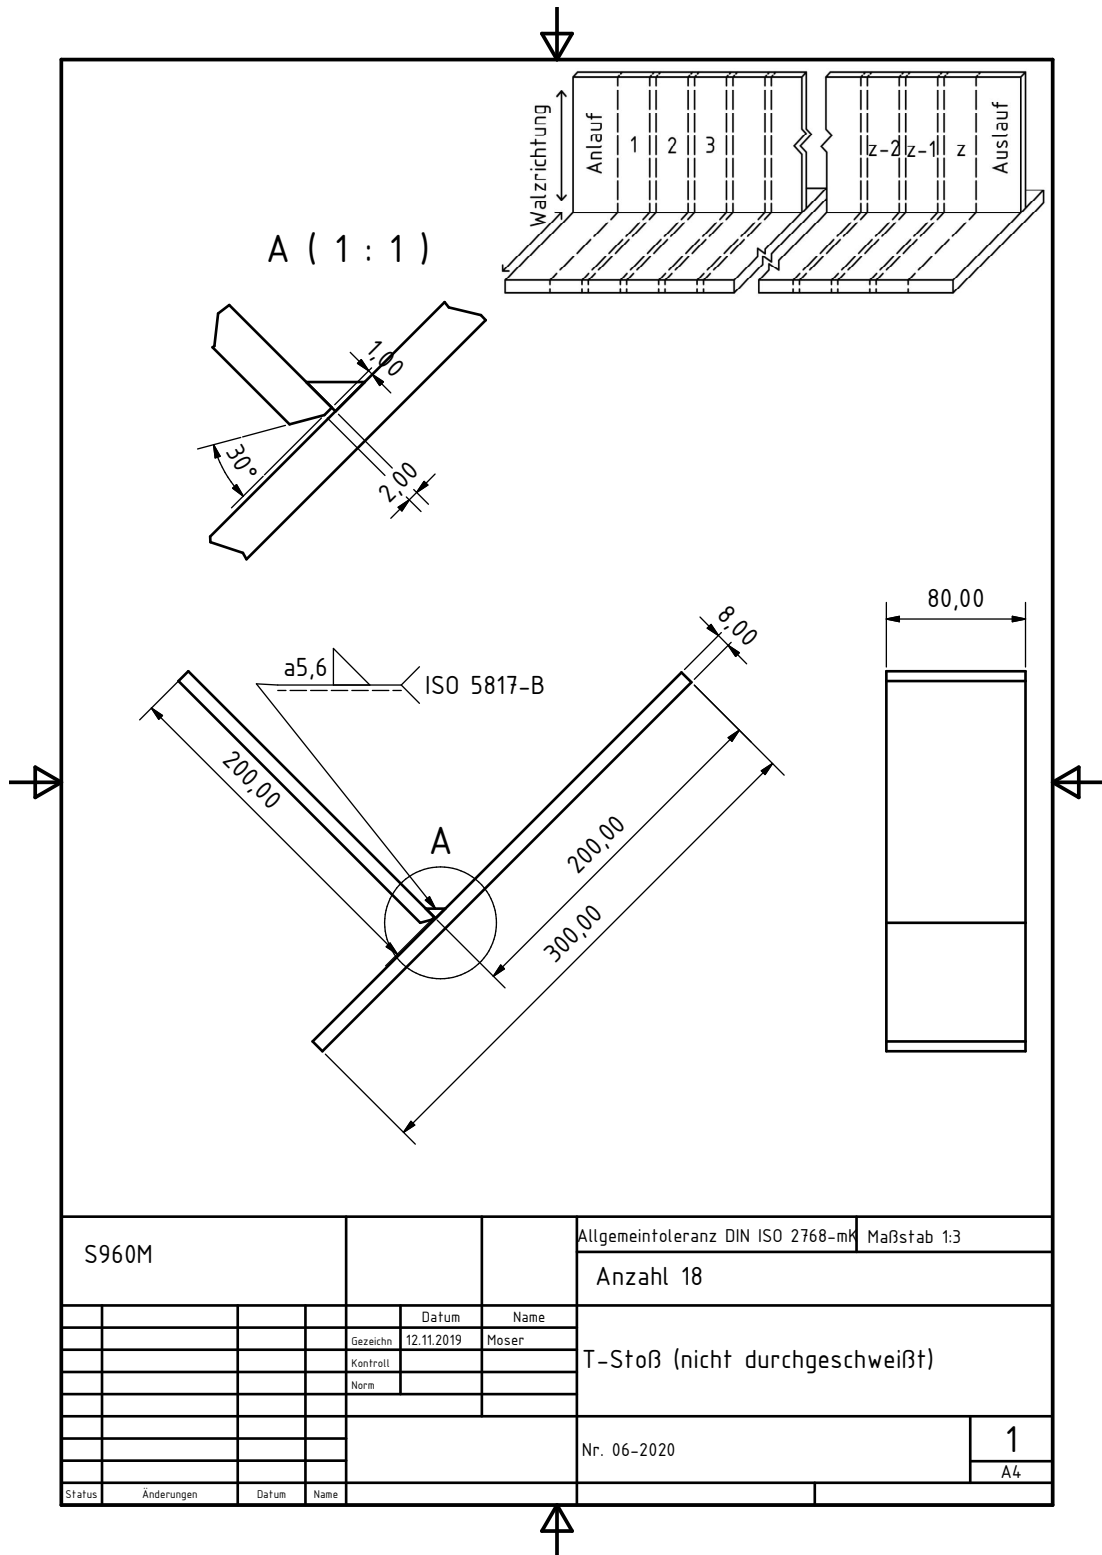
Fertigungszeichnung für die T-Stoß Proben aus S960M.
